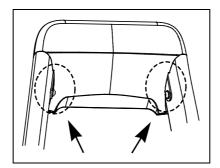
apriete de los cierres delanteros del soporte de la columna central
